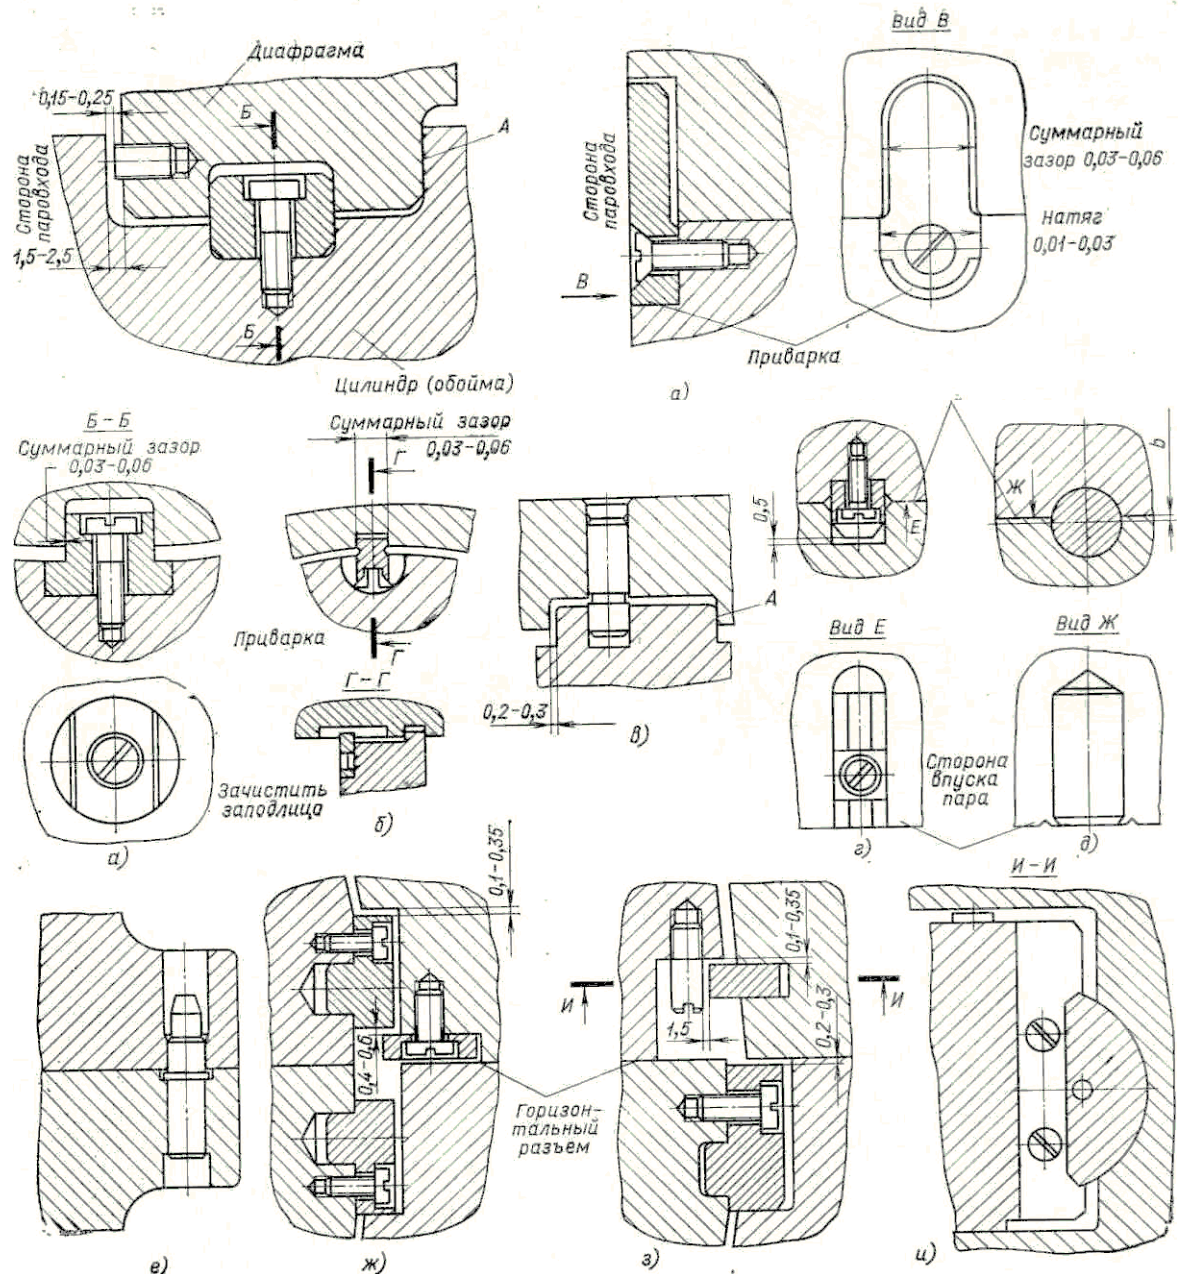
Детали крепления диафрагмы в цилиндре или обойме:
